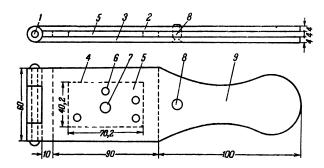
Листовой кондуктор для сверловки деталей конденсатора переменной емкости.
